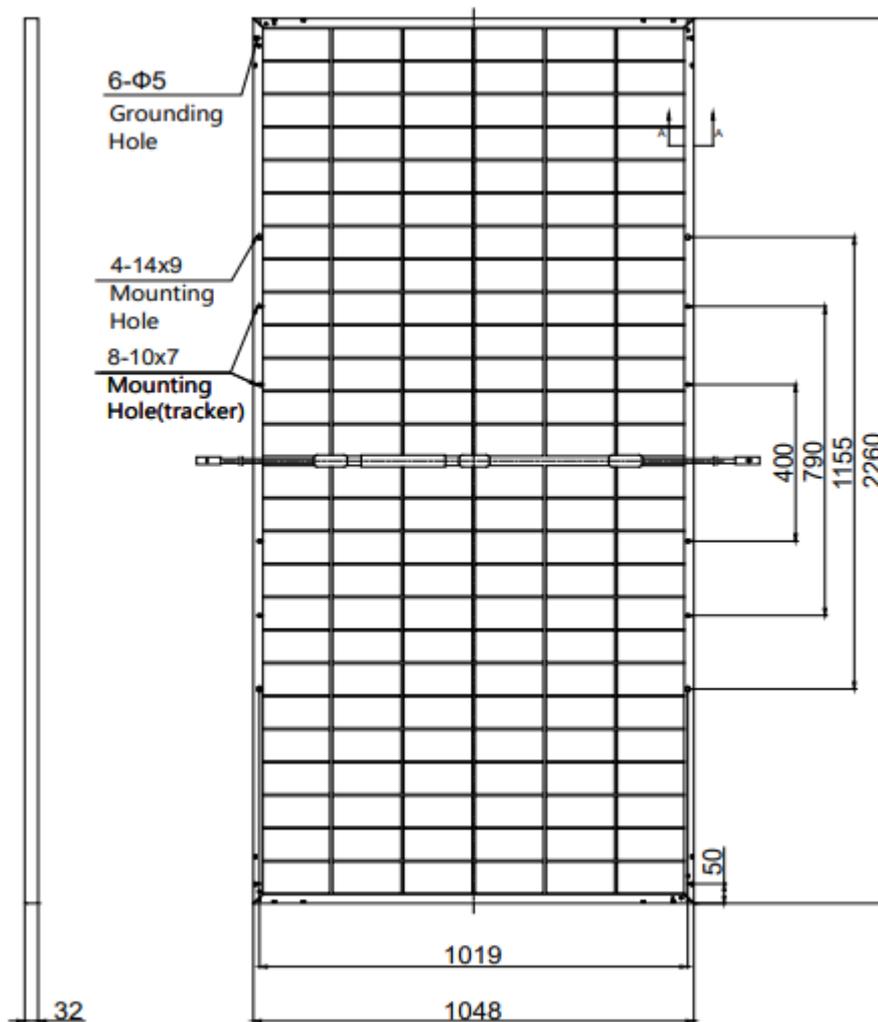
Dimensiones del panel bifacial 2260x1048 (mm)
